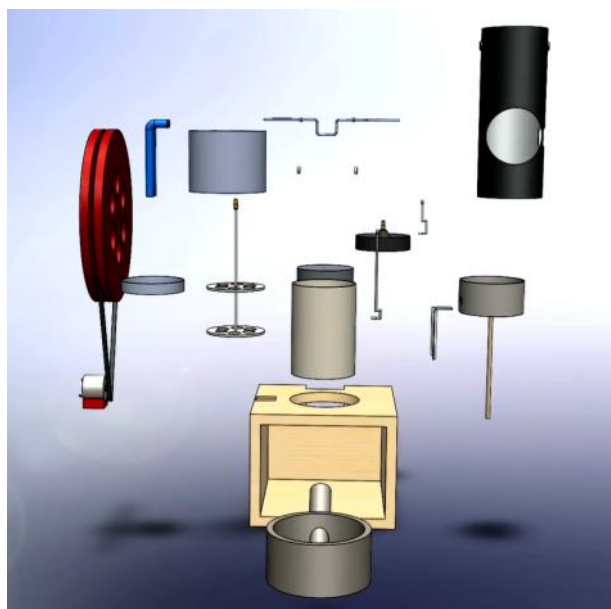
Детализовка модернизированного двигателя Стирлинга
